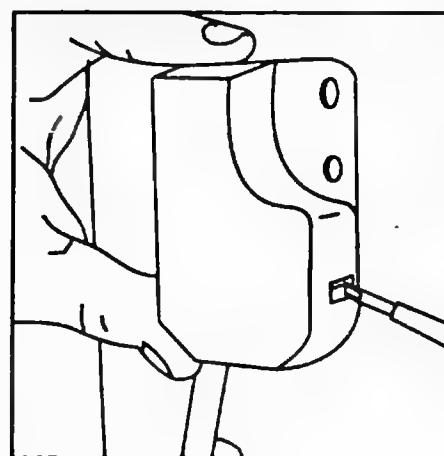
Демонтаж крышки клеммной коробки
